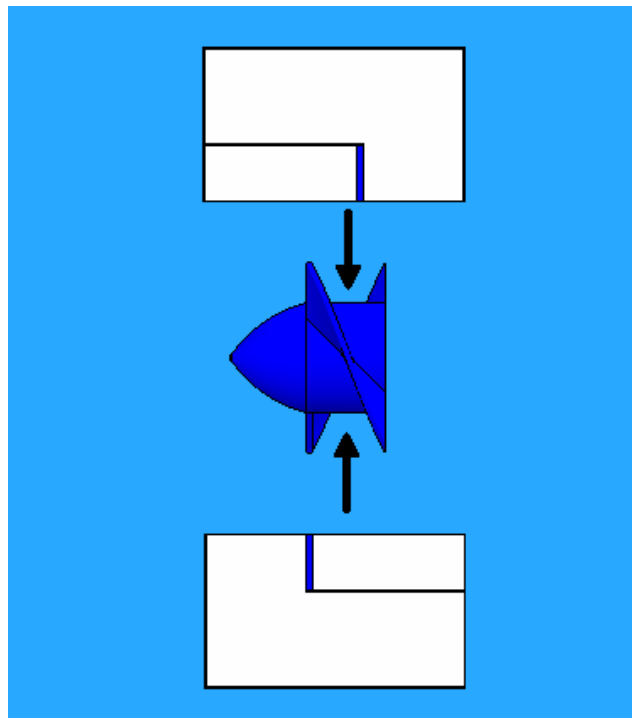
Sujeción de dos álabes, previo a la soldadura, parte II.
